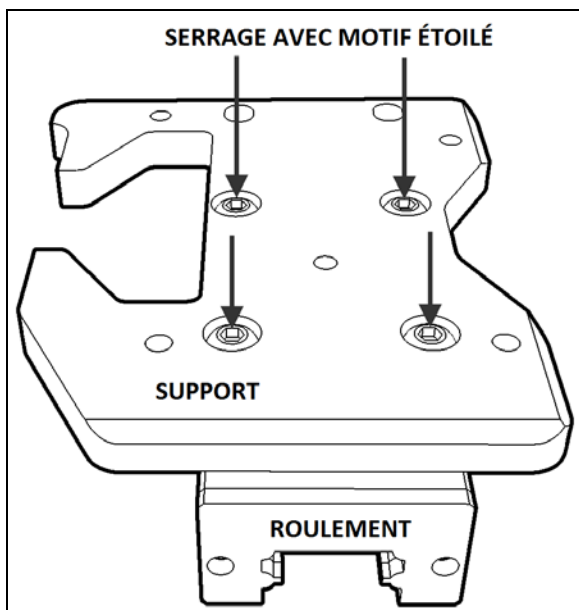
VIS DE MONTAGE DU PALIER 26158
